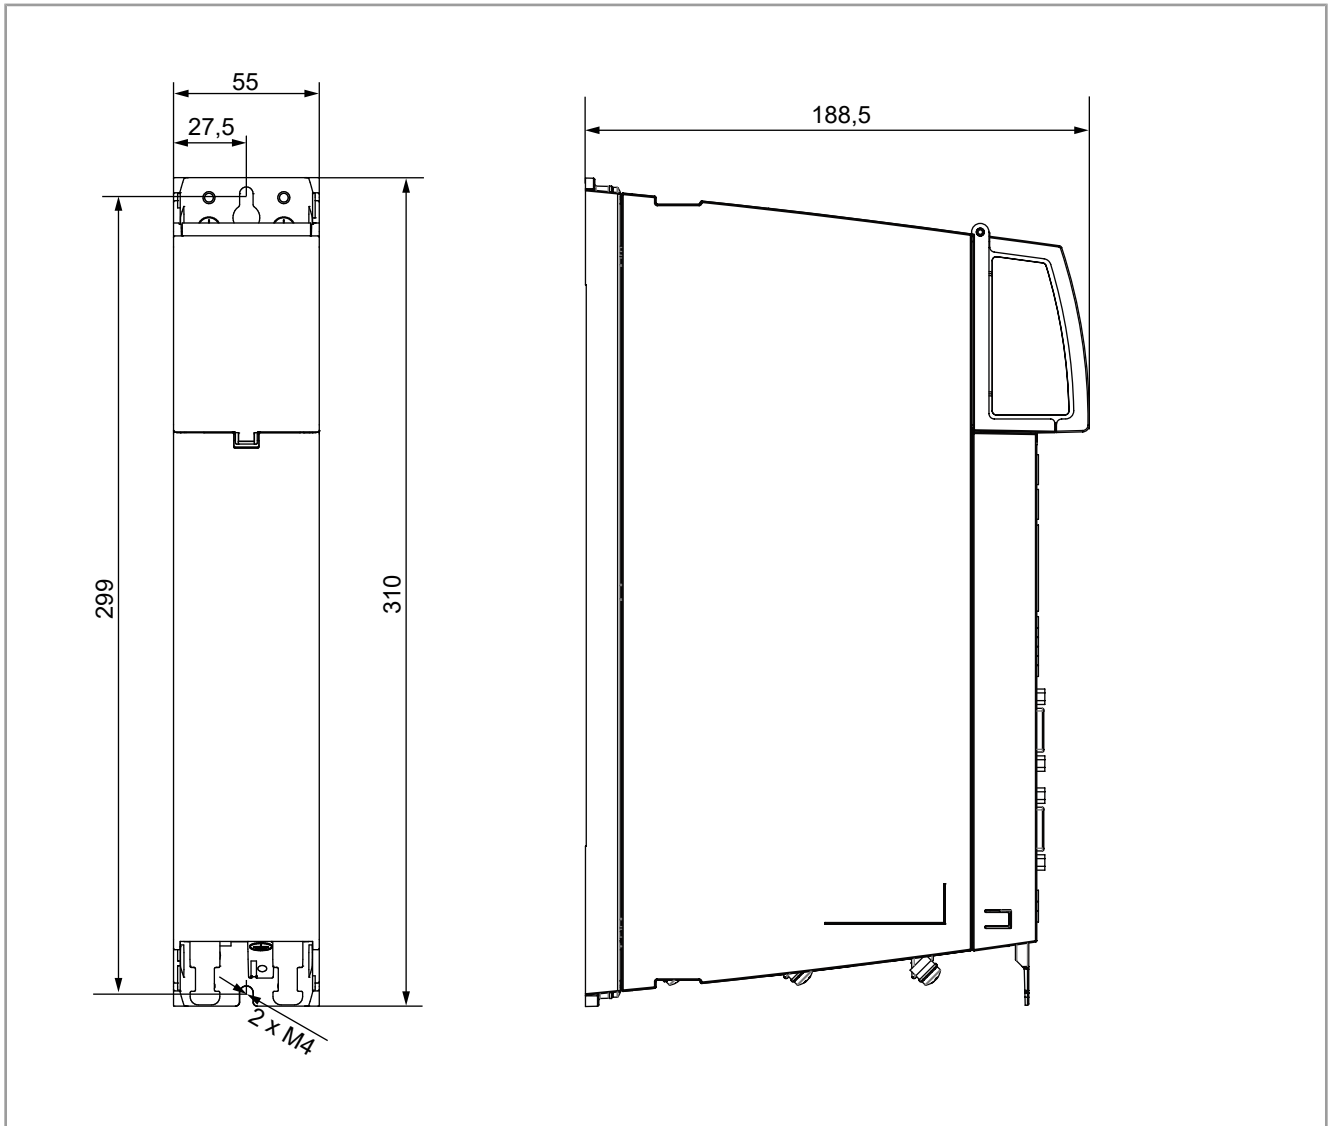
Abmessungen BG1 in mm Cold Plate Montage
